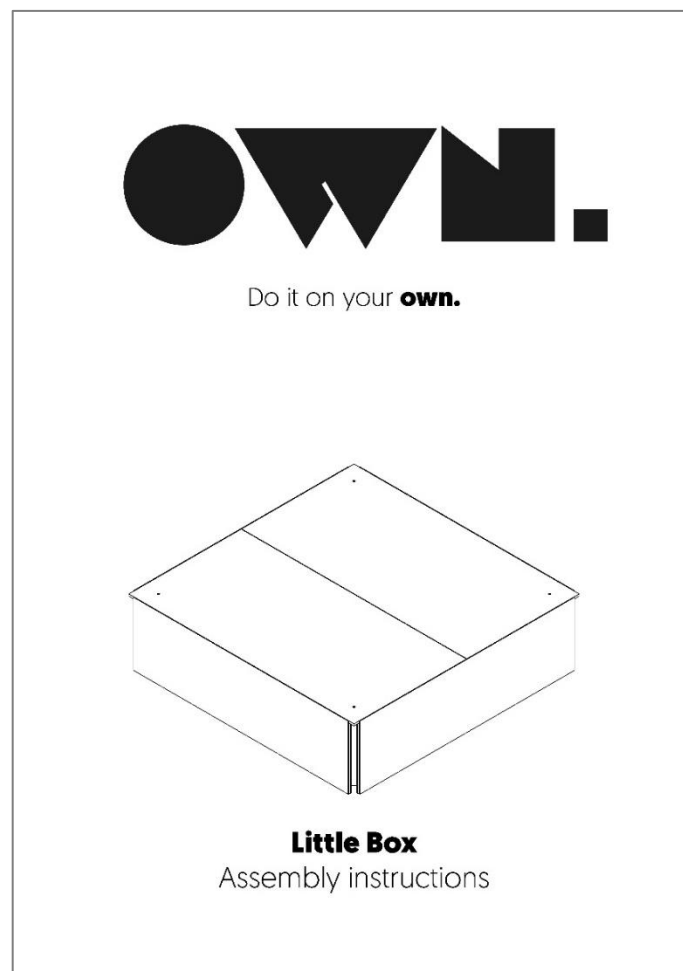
Extracto del Manual de montaje del Box Pequeño
